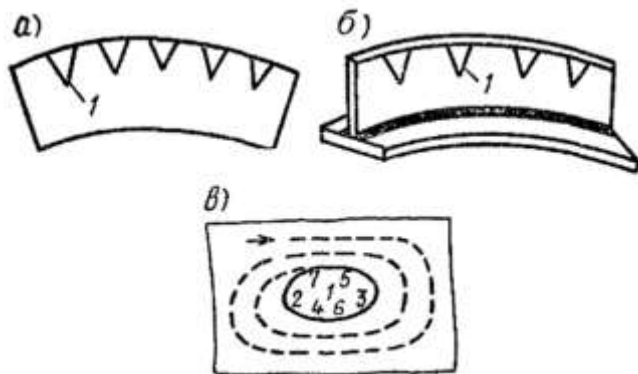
Термическое исправление деформации: а — серповидность листа; б — изгиба сварного тавра; в — хлопуна.
